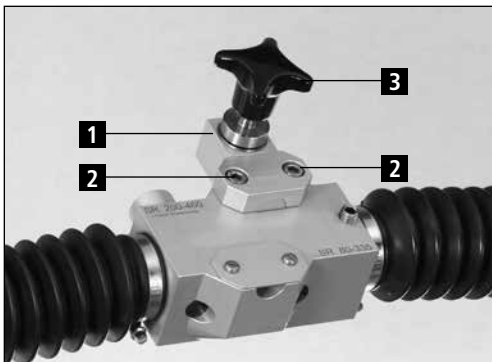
Drehbar gelagerter Aufnahmekopf
